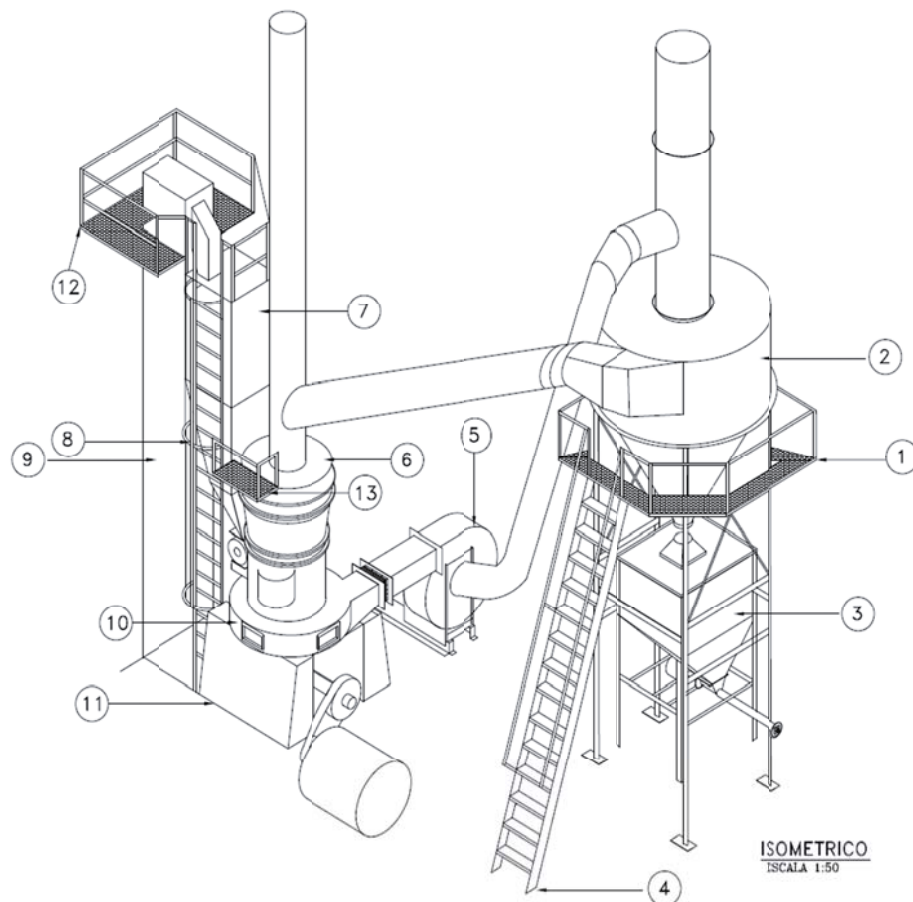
Planta de molienda instalada en New Tech Agro S.A.
